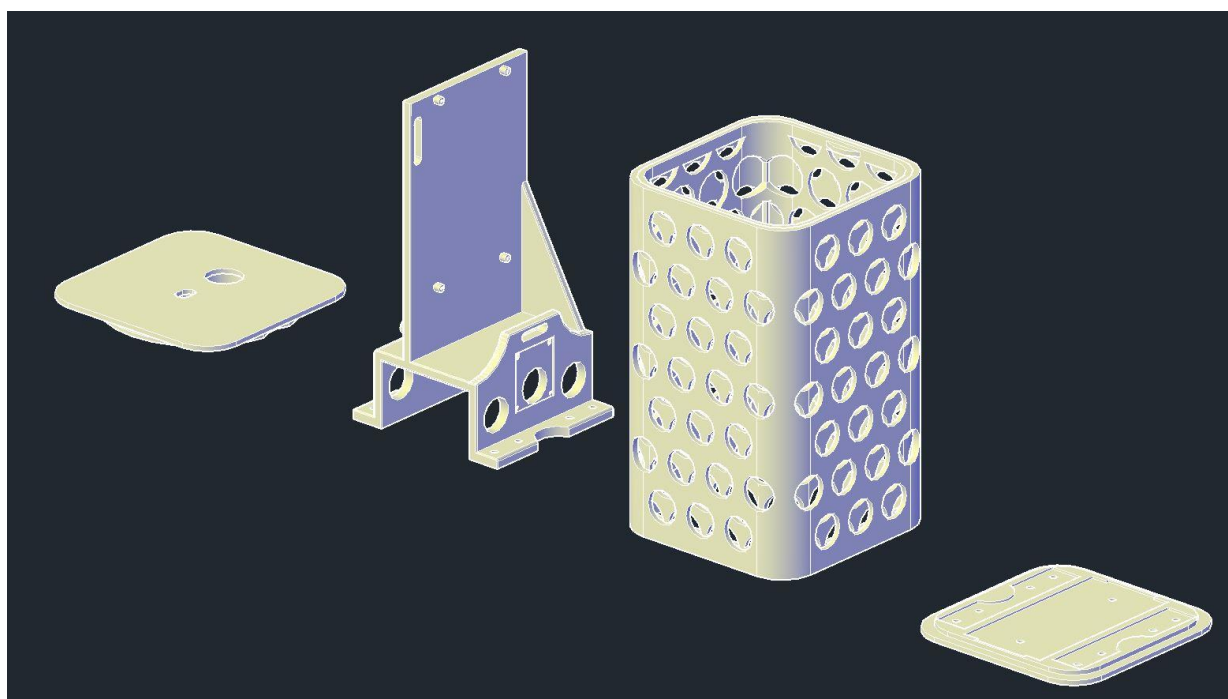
Конструкция корпуса газоанализатора, вид под углом
